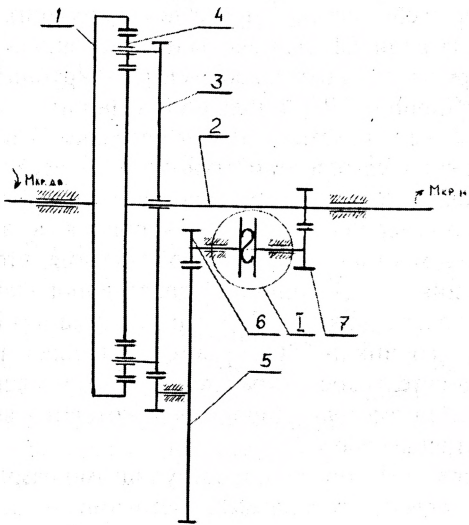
Двухпоточная бесступенчатая передача: I — механизм управления; 1 — ведущее колесо; 2 — ведомое колесо; 3 — водило; 4 — сателлиты; 5 — блок передаточных колес; 6, 7 — входящее и исходящее колеса механизма управления
